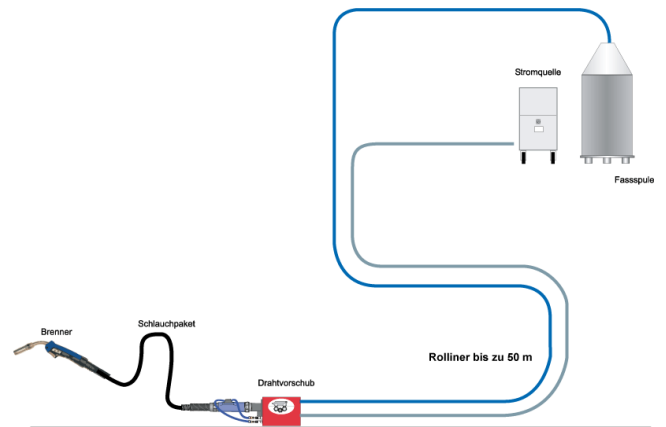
Handschweißanlage mit Fassdrahtversorgung
